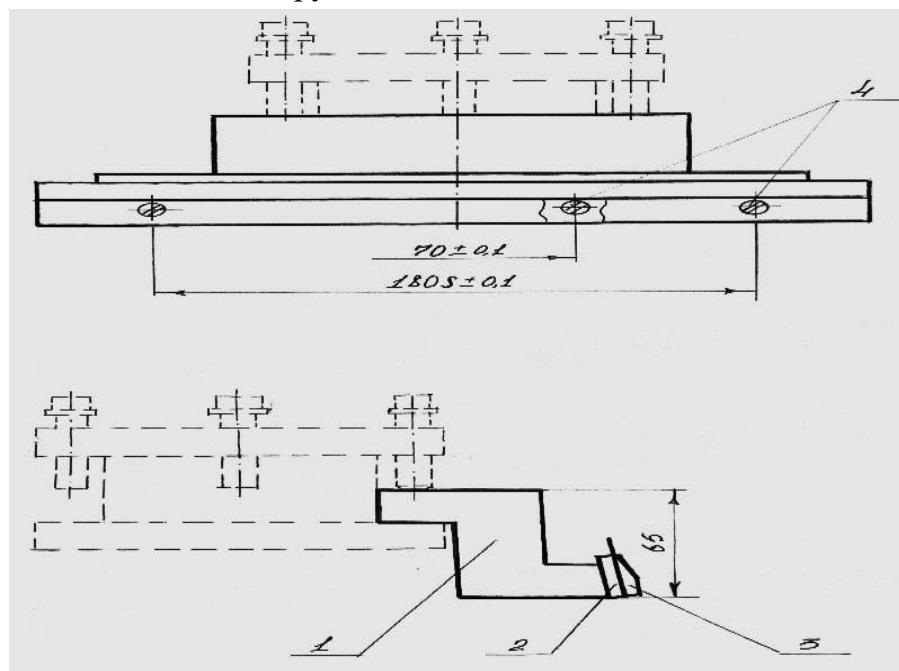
Опытная установка для подготовки к работе тонких пластинчатых ножей .1 – ножодержатель; 2 – заточной вал; 3 – резцедержатель станка.
